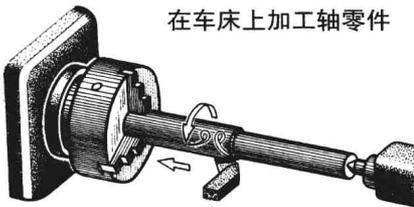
装配体、装配图, 零件、零件图及依据图样加工零件
